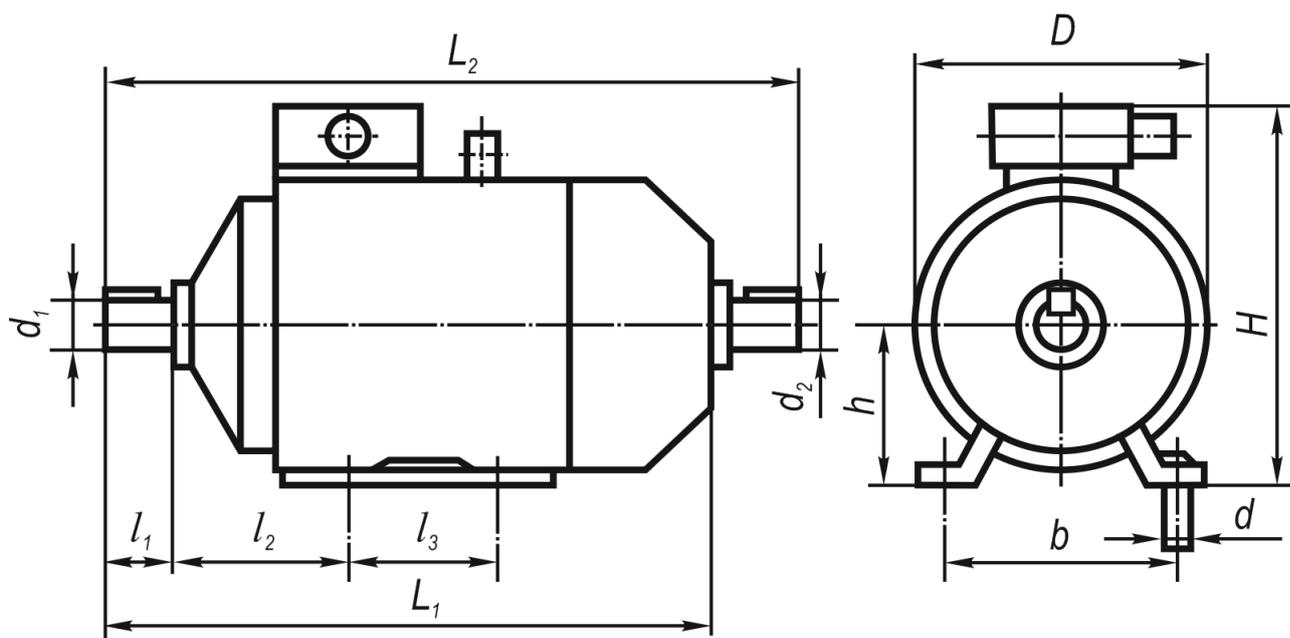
Основные габаритные размеры электродвигателей
